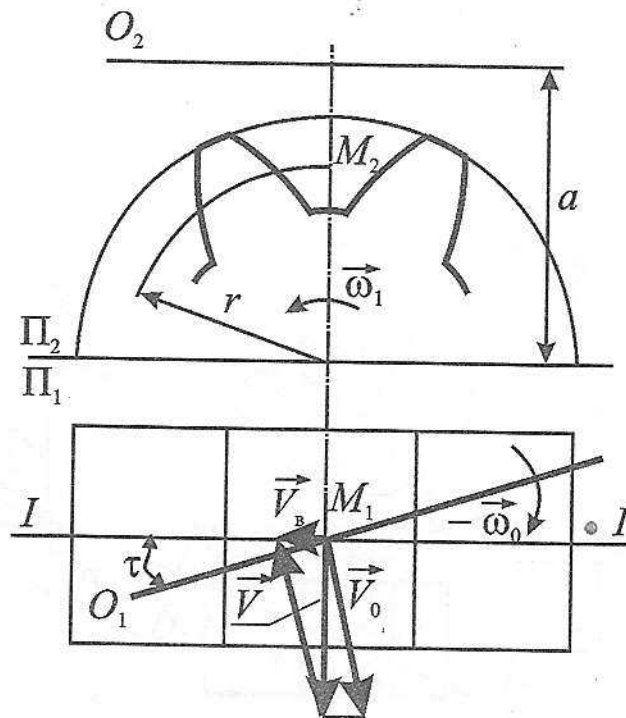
Схема формообразования обкаточными дисковыми фрезами многозубых деталей
